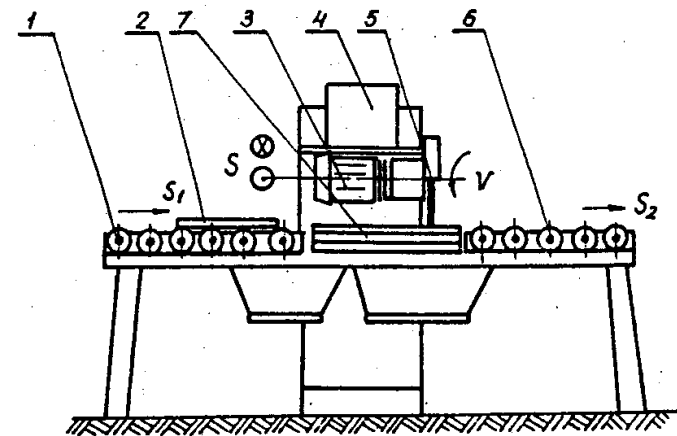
Схема поперечно-окантовочного станка СМР-080:
